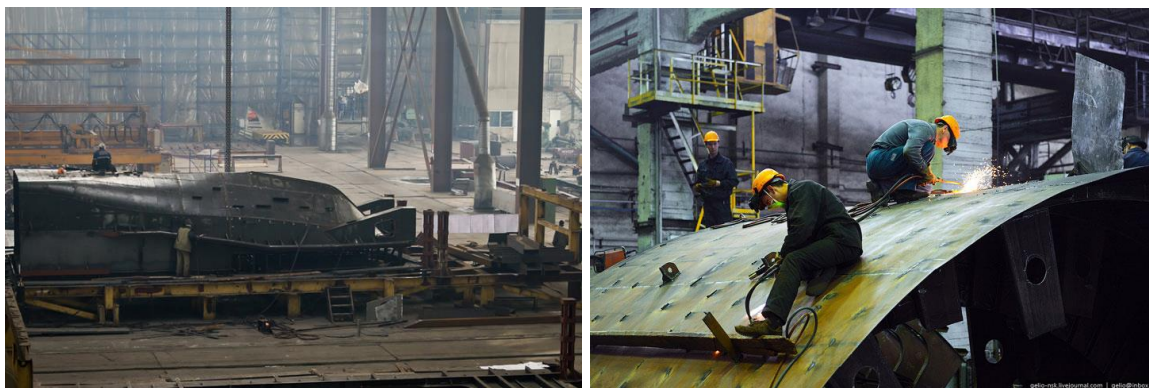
К задаче № 2.1.4. Сварка корпуса судна на судовой верфи
